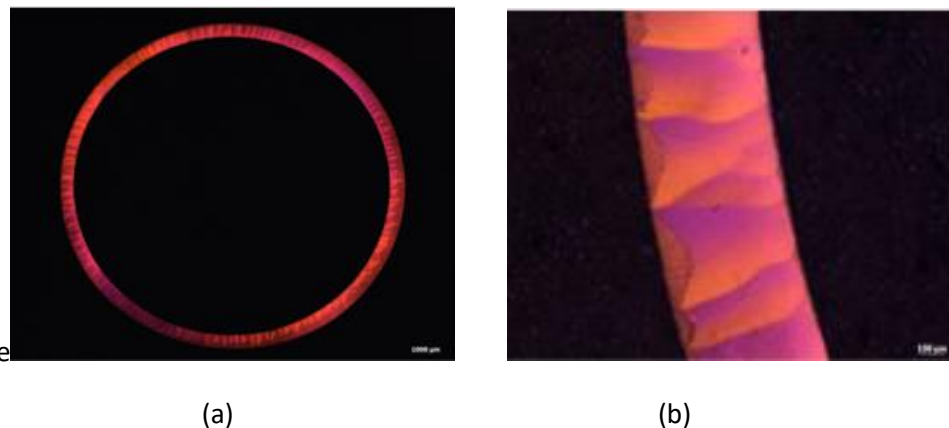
(a) Vista em corte do tubo eletroformado e estanque para uso em ultra-alto vácuo. (b) Detalhe da deposição.
